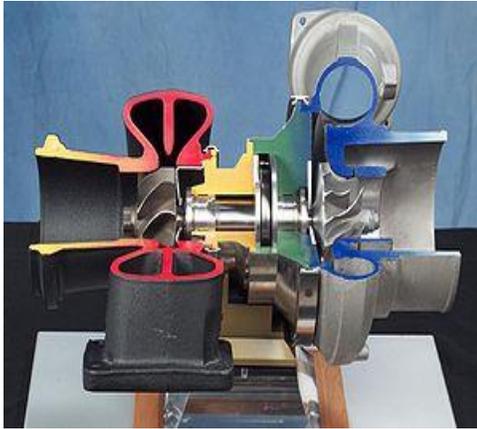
Sección de un turbocompresor y turbocompresor completo
